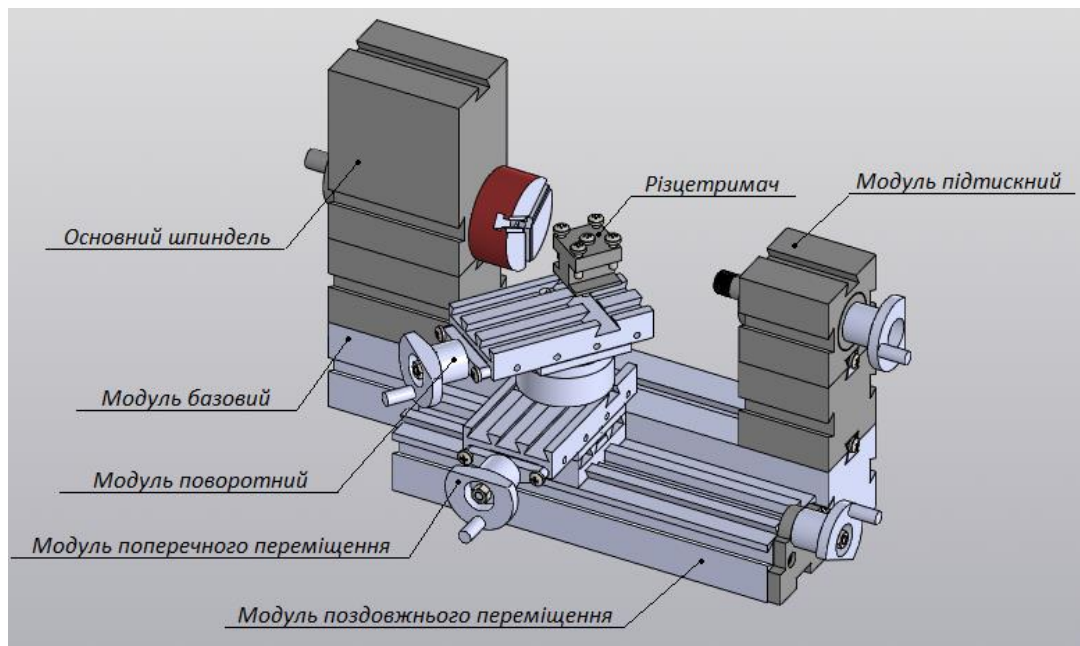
Багатокоординатний токарний верстат у зборі
